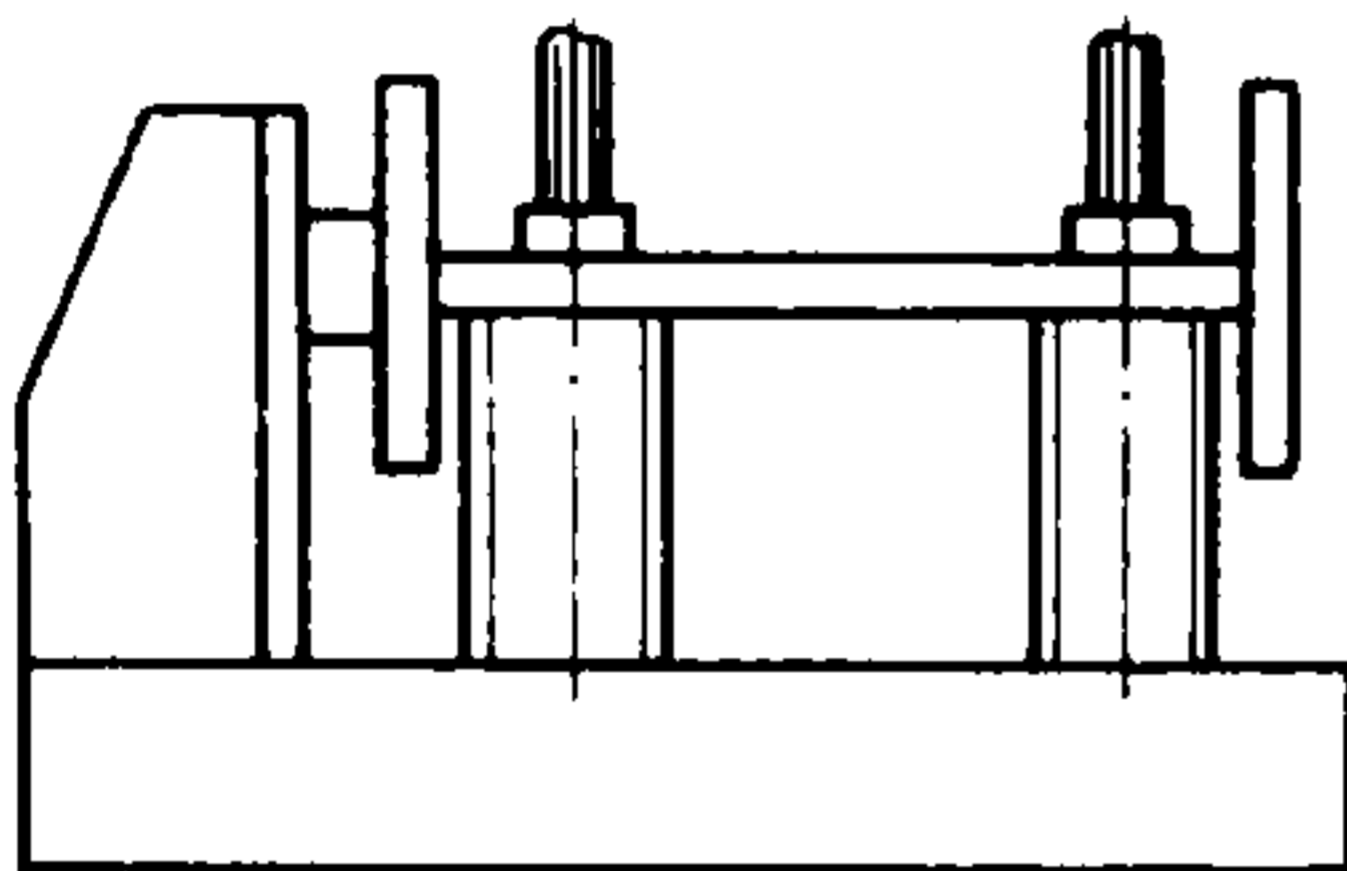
Установка стержня двутаврового сечения на столе торцефрезерного станка
